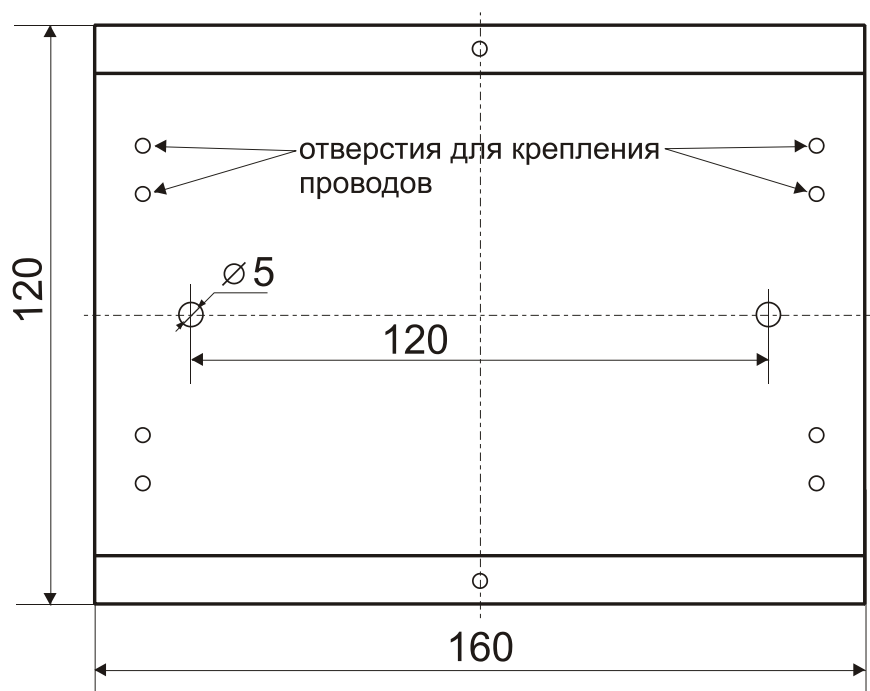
Габаритные и установочные размеры SF-AMC-22-A
